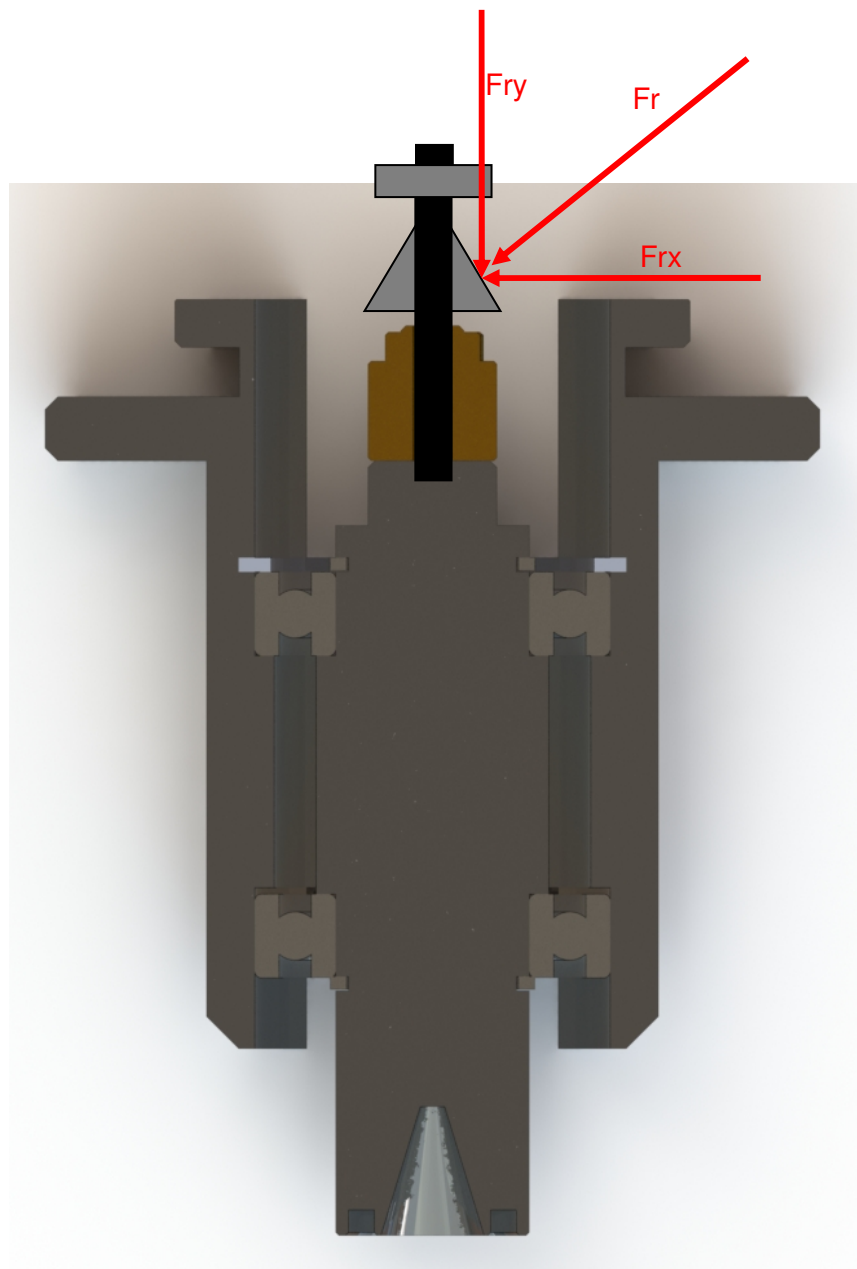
Werkzeughalter 1 Schnittansicht 4
